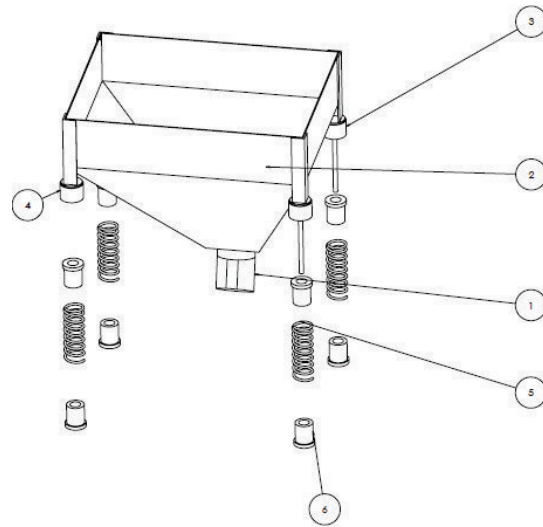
Vista explosionada- Tolvas de almacenamiento
